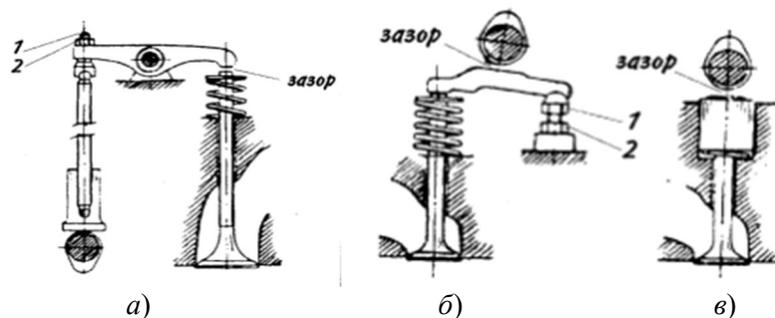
Распространенные виды ГРМ и места контроля теплового зазора: а – с нижним расположением распредвала и приводом клапанов через штанги и коромысла; б – с верхним расположением распредвала и приводом клапанов через рокеры; в – с расположением кулачков распредвала непосредственно над клапанами и приводом клапанов через цилиндрические толкатели; 1 – регулировочный винт; 2 – контргайка
